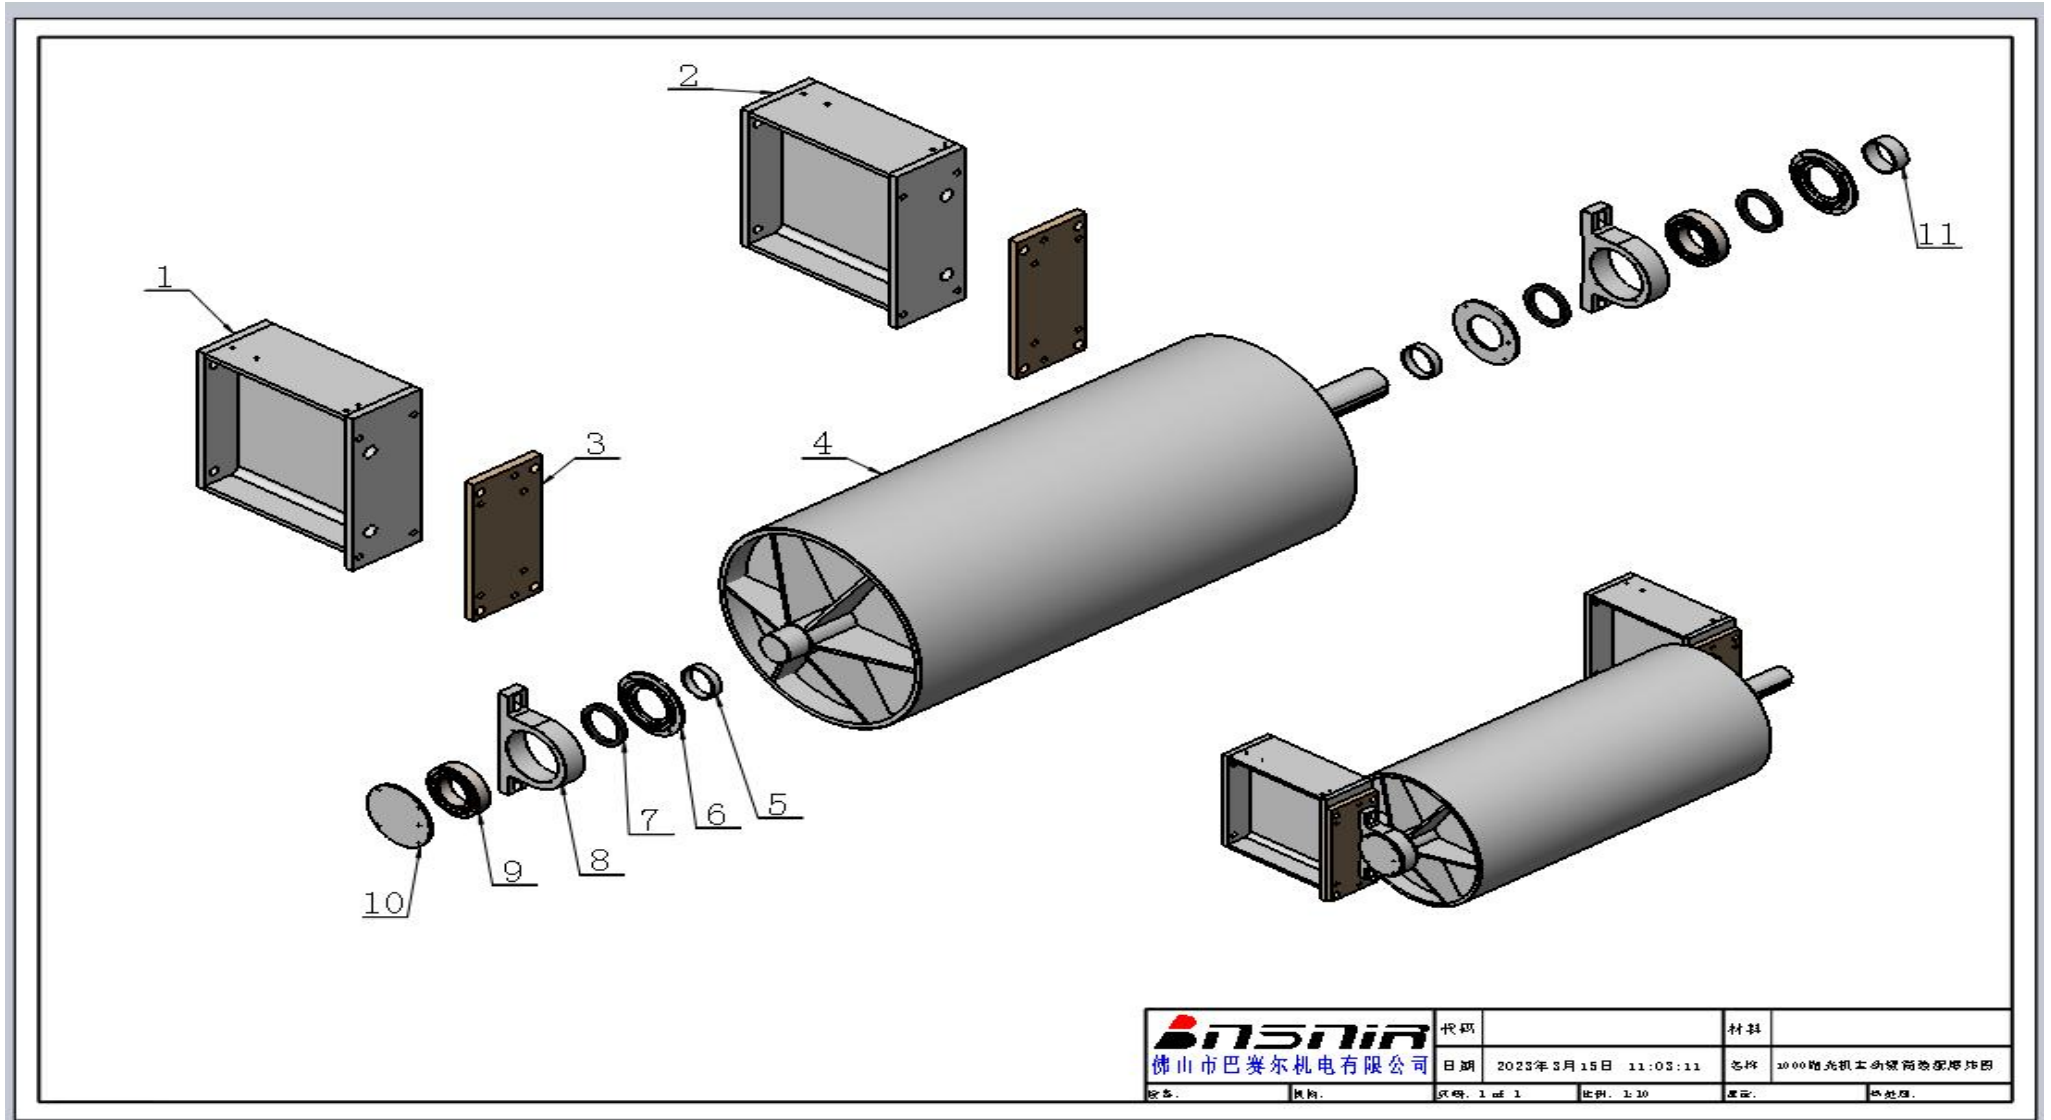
7 机架部分——主动辊筒组件装配图 picture2-7 Gantry Part -- Assembly drawing of the drive roller assembly
